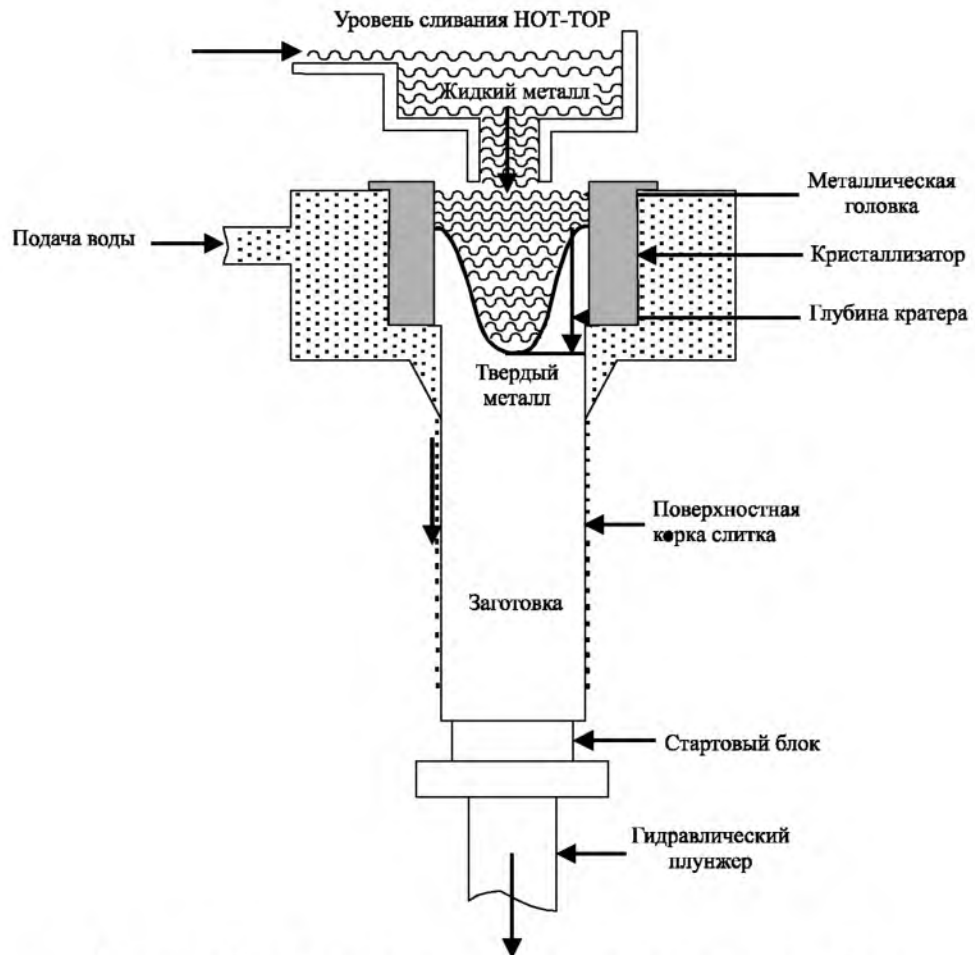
Схема непрерывной разливки столбов (заготовок) с прямым охлаждением
